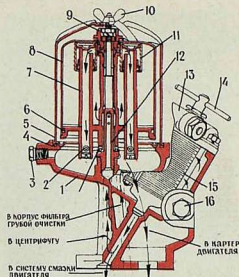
Масляные фильтры двигателя ЗИЛ-130: 1 — корпус масляных фильтров; 2 — жиклер центробежного фильтра тонкой очистки (центрифуга); 3 — пробка; 4 — прокладка конуса; 5 — конус; 6 — уплотнительное кольцо; 7 — корпус фильтра тонкой очистки; 8 — крышка корпуса; 9 — гайка; 10 — гайка-барашек; 11 — сетчатый фильтр; 12 — ось; 13 — крышка фильтра грубой очистки; 14 — рукоятка; 15 — фильтр грубой очистки; 16 — пробка для слива масла из фильтра грубой очистки.
